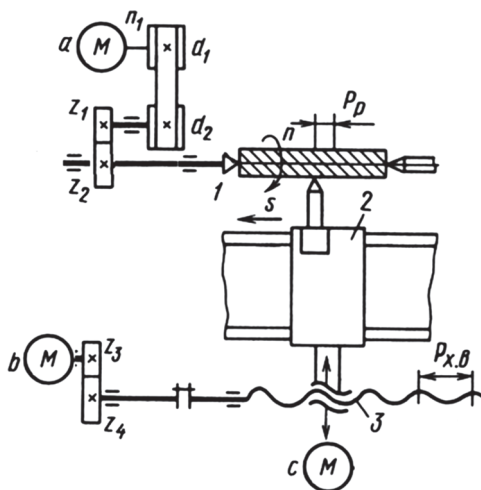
Упрощенная кинематическая схема токарного станка с ЧПУ:
